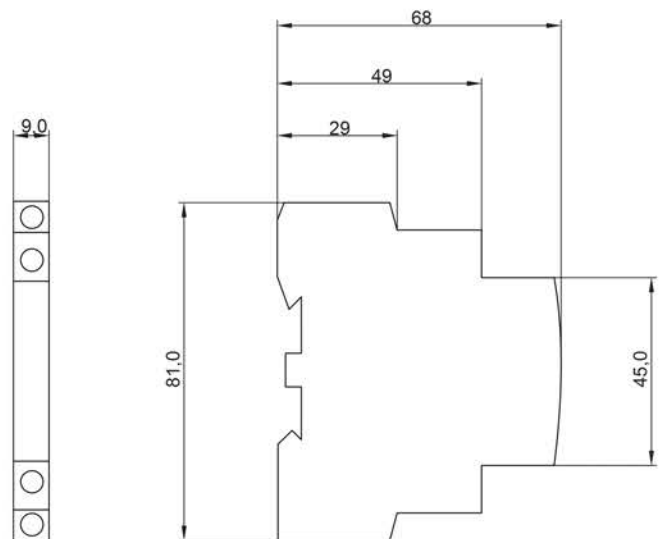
Габаритные размеры дополнительных контактов типа 1HO, 1H3, 2H3 и 2HO / Figure 7 – Dimensions of auxiliary contacts of 1HO, 1H3, 2H3 and 2HO types
